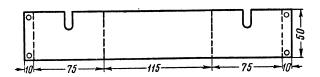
Чертеж скобы для крепления барабана переключателя.
